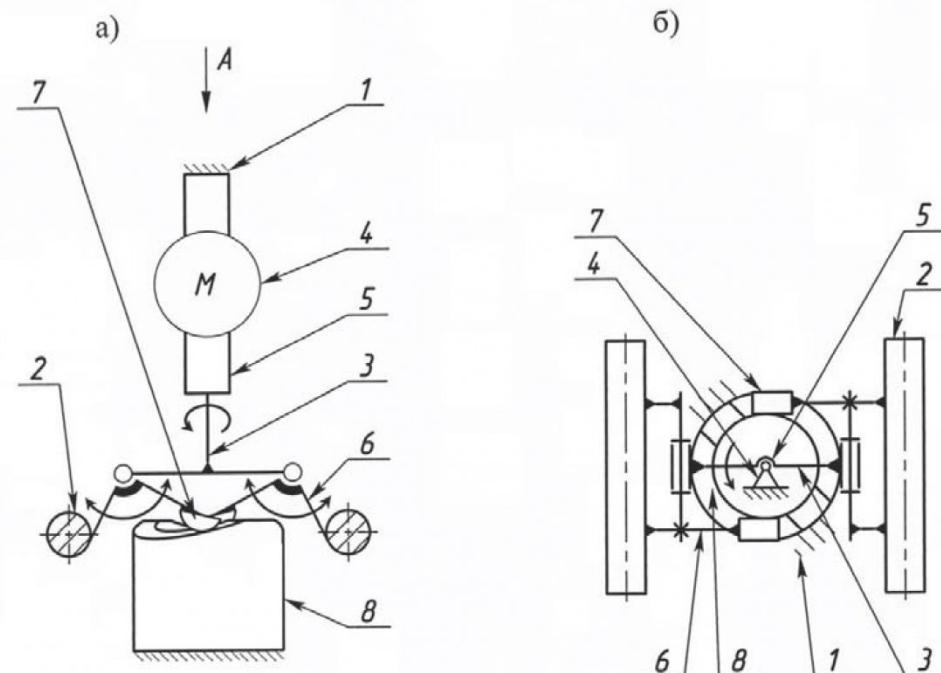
Торцевой кулачковый механизм вибродвижителя с преобразованием вращательного движения в поступательное [2]: а) общий вид; б) вид по стрелке А на а); 1 - стойка; 2 - инерционные массы; 3 - приводной вал; 4 - двигатель; 5 - подшипниковая опора; 6 - двухлечье рычаги с инерционной массой на одном плече и дуговым или роликовым (для уменьшения силы трения) толкателем 7 на другом; 8 - торцевой кулачок, жестко связанный со стойкой (платформой транспортного средства)
